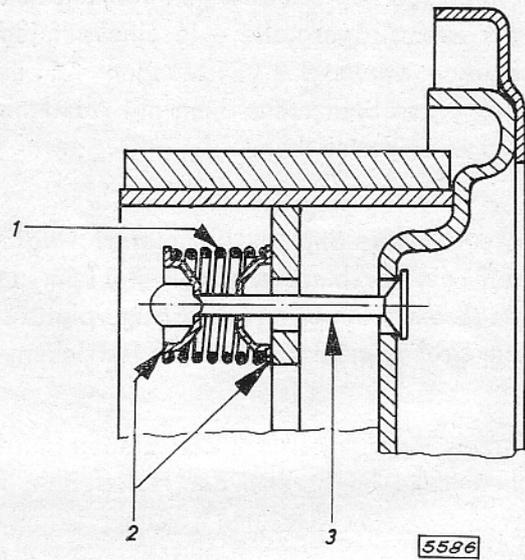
Bremsbacke an Bremsträgerplatte befestigt
